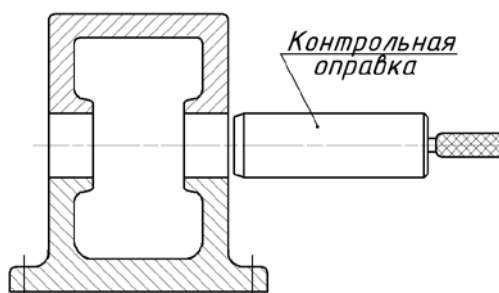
Схема проверки соосности отверстий корпуса редуктора
